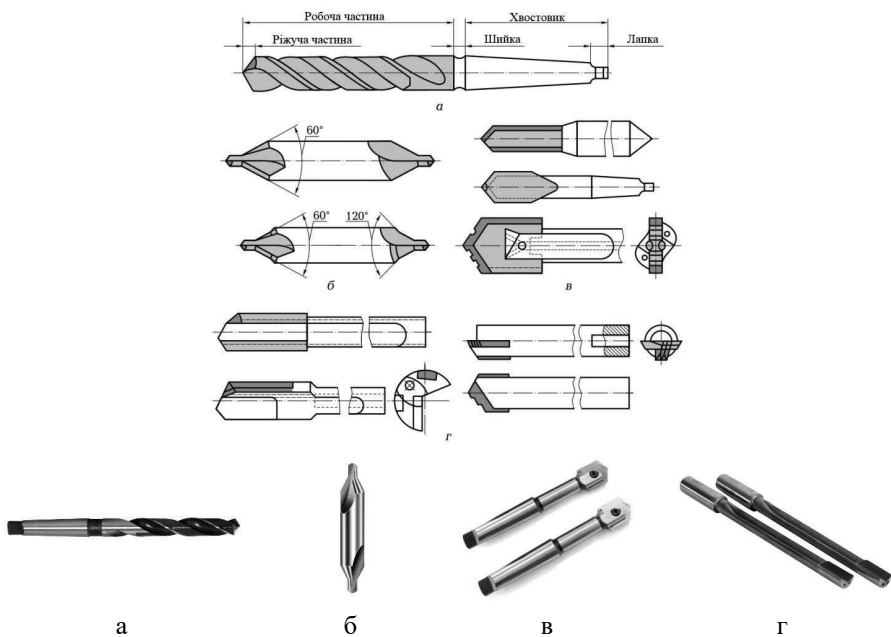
Свердла для обробки отворів: а – спіральні; б – центрувальні; в – перові; г – рушничні для глибокого свердління
